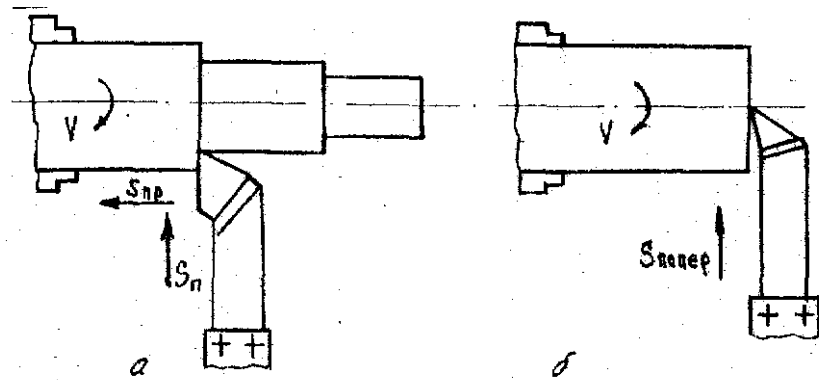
Схеми різання на токарних верстатах: а) обточування ступінчастих валів; б) підрізання торця
